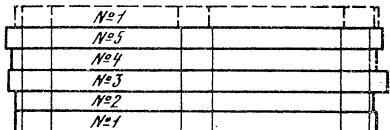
Схема сравнительного контроля точности разметки заготовок
